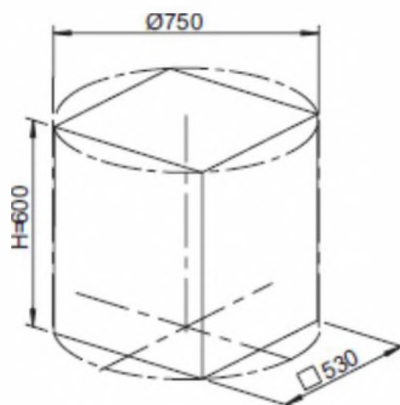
Габаритні розміри деталі при положенні столу 45°
